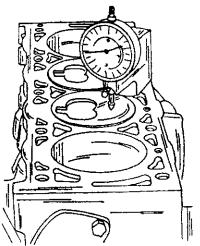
Переместить измерительный штифт как можно ближе к центру дна поршня. Индицируемое значение является выступом поршня над поверхностью блока цилиндров.
